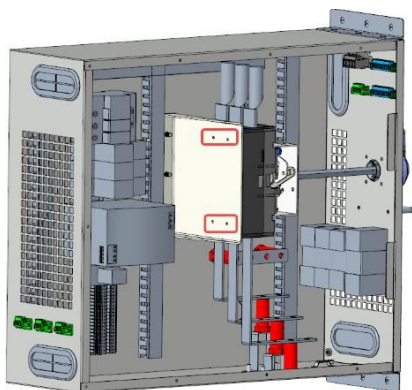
45 Remova os parafusos de fixação do disjuntor e remova o disjuntor
